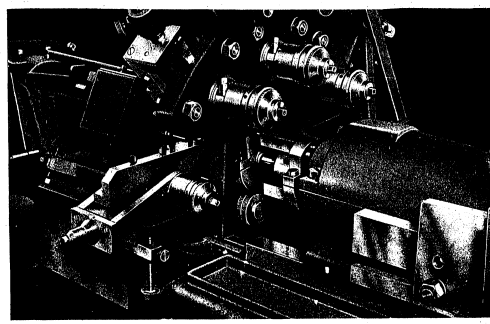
SEITENANSICHT DER FÜHRUNGSBÜCHSE DES HP-UT
